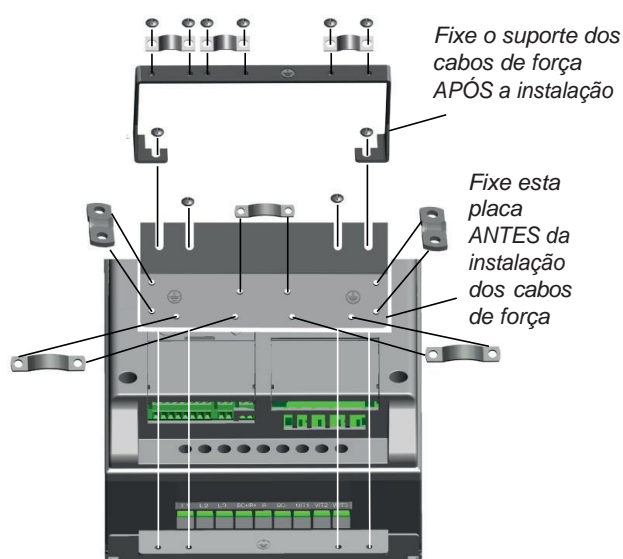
Instalação da placa PE e suporte a cabo API, MI4 - MI5
